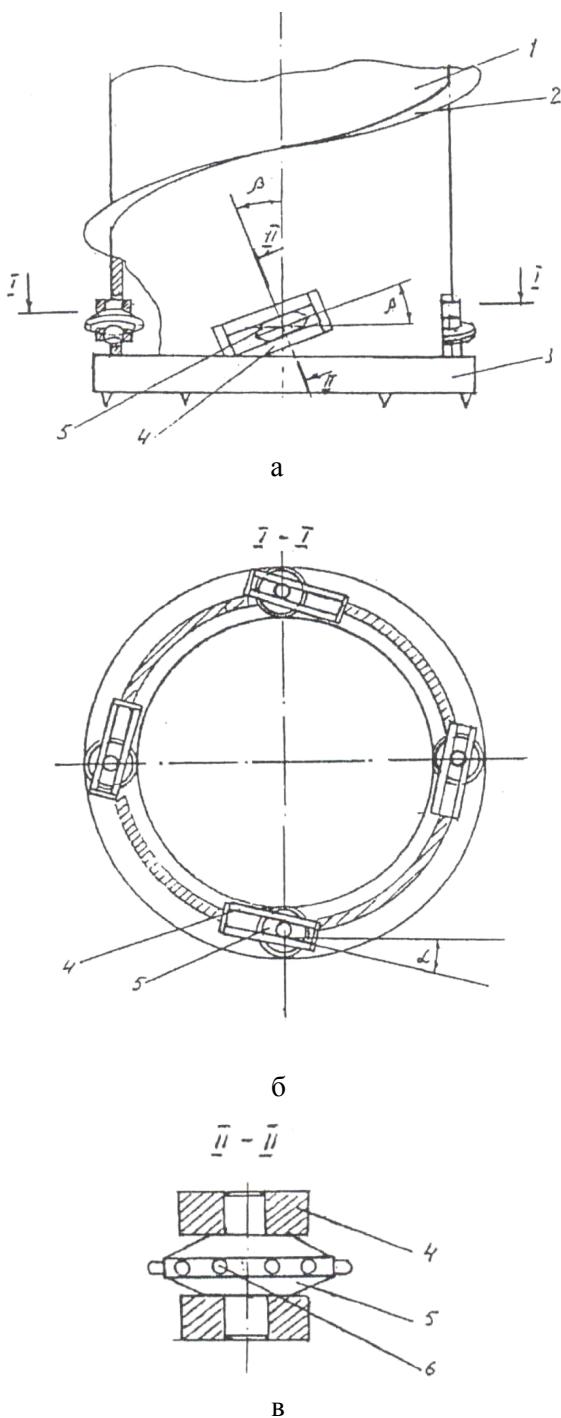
Схема кільцевого бура з роликовим пристроєм: а – вид збоку; б – розріз I-I; в – розріз II-II
